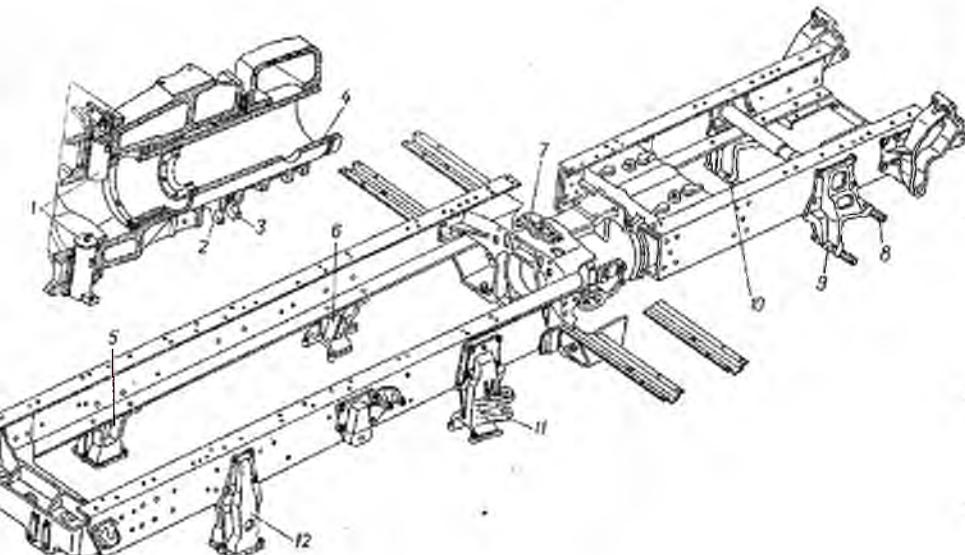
Рама трактора ЛТ-171: 1 — вісь вертикального шарніра; 2 — корпус шарніра; 3 — бутиль задньої опори шарніра; 4 — труба горизонтального шарніра; 5 — кронштейн ресори передній правий; 6 — кронштейн ресори задній правий; 7 — кронштейн слідкуючої тяги; 5 — болт; .9 — кронштейн заднього моста лівий; 10 — кронштейн заднього моста правий; 11 — кронштейн ресори задній лівий; 12 — кронштейн ресори передній лівий
